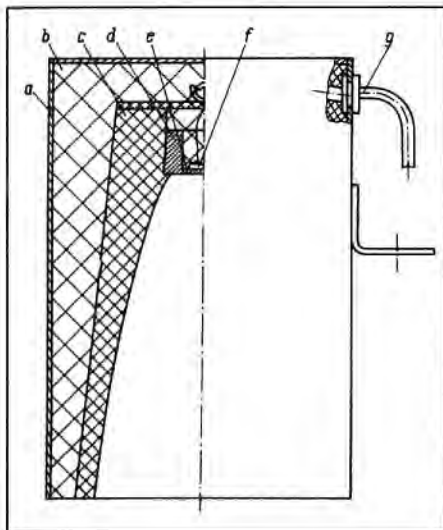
Aufbau des Ultraschall-Meßkopfes; a Blechmantel, b Weichschaum, c PUR-Hartschaum, d Ultraschall-Wandler-Stützkörper, e Plattenschwinger, f Erreger (Piezo-Platte), g Anschluß Koaxialkabel
